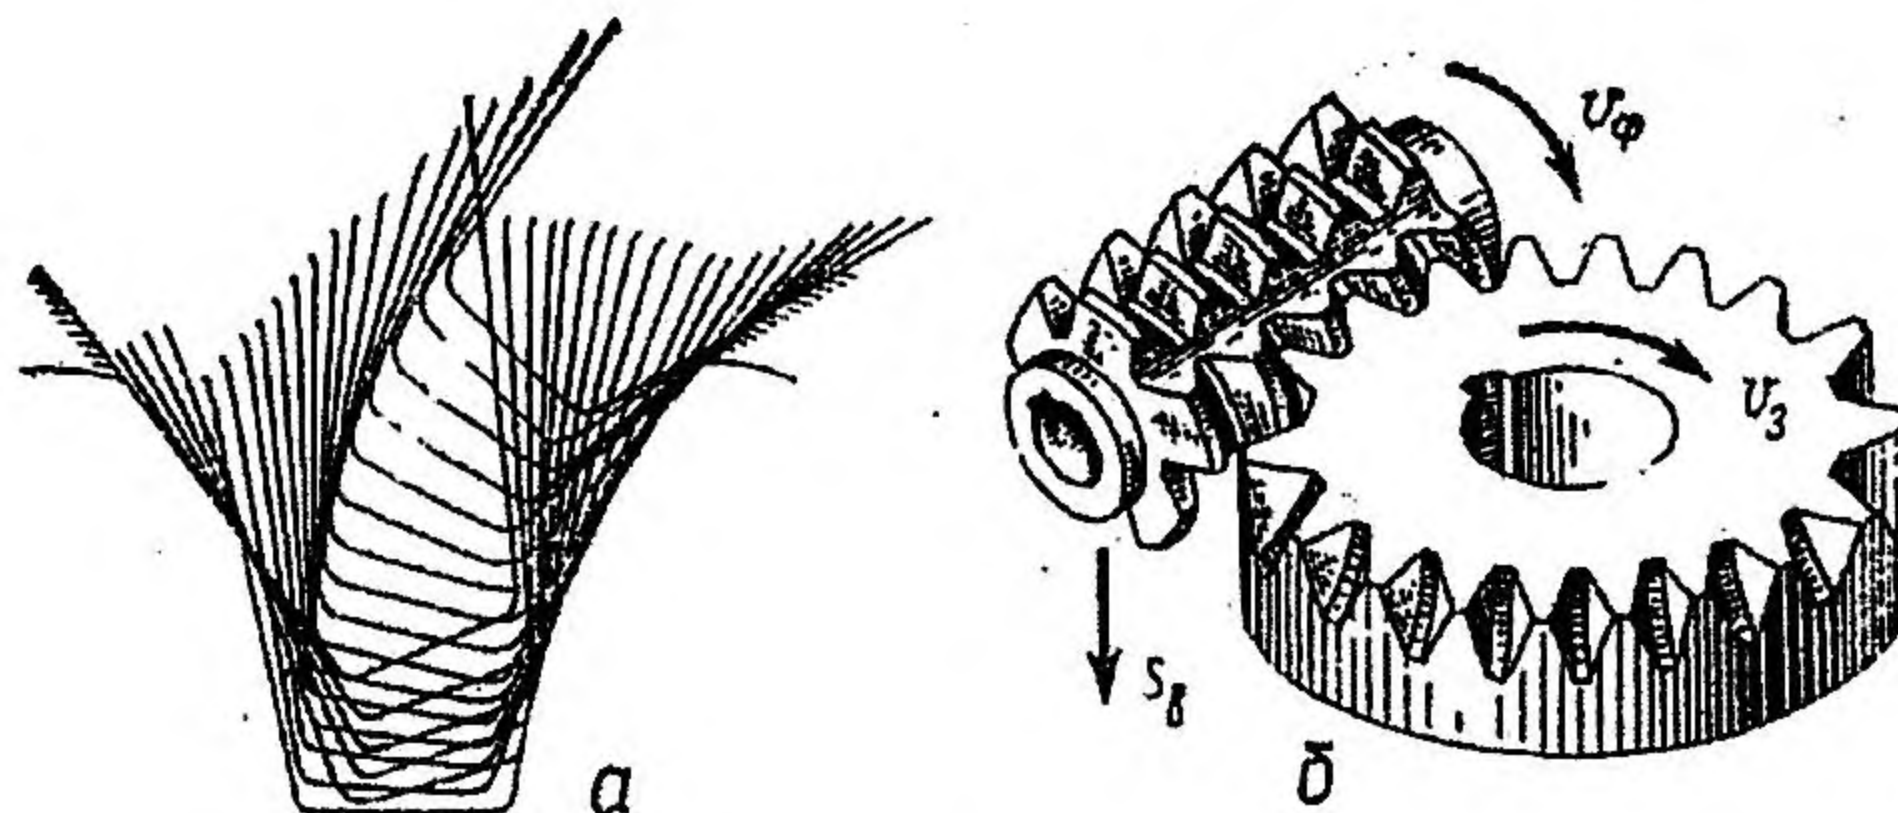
Схема нарезания зубчатых колес червячной модульной фрезой:
